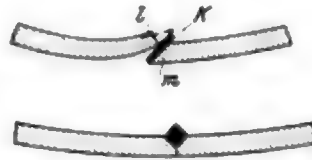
Schweißen des vorderen Kesselschusses mittels eines Keilstückes.
